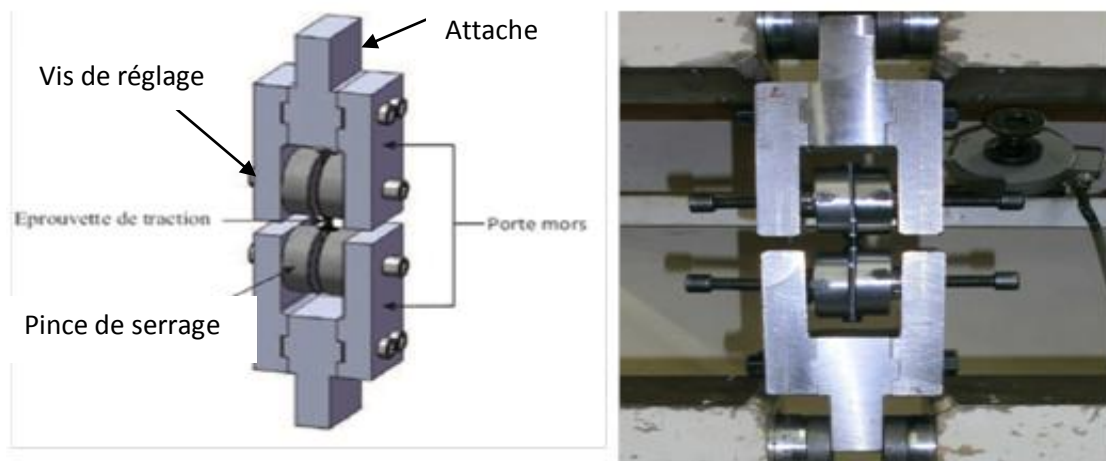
Dispositif de traction adapté aux éprouvettes
